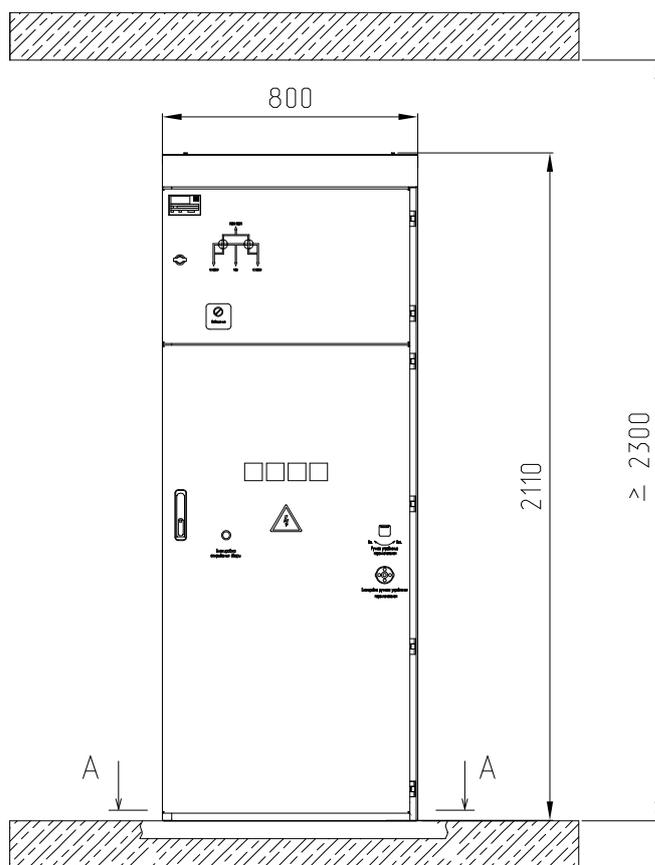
Ячейка заземляющего разъединителя РУОШ-600-ЗР-УХЛ4
